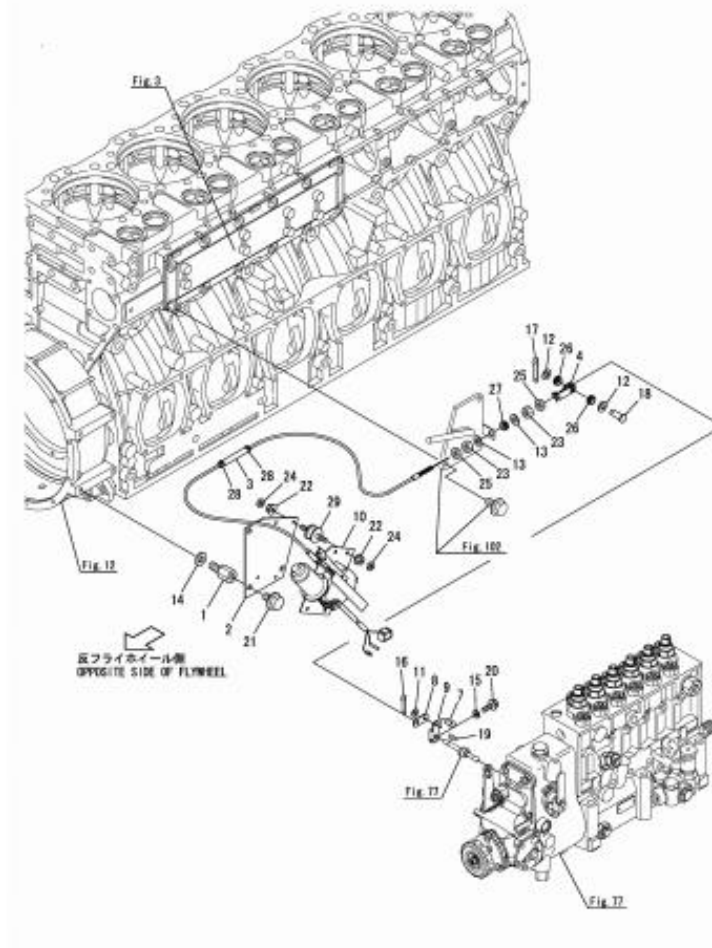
Dispositivo de parada - Solenoide del motor – JCI: Acero y Aluminio
